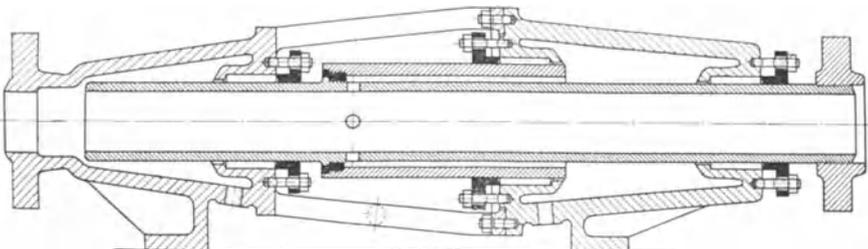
Rohrkompensator für Höchstdruckdampf von Franz Seiffert & Co., Berlin.
